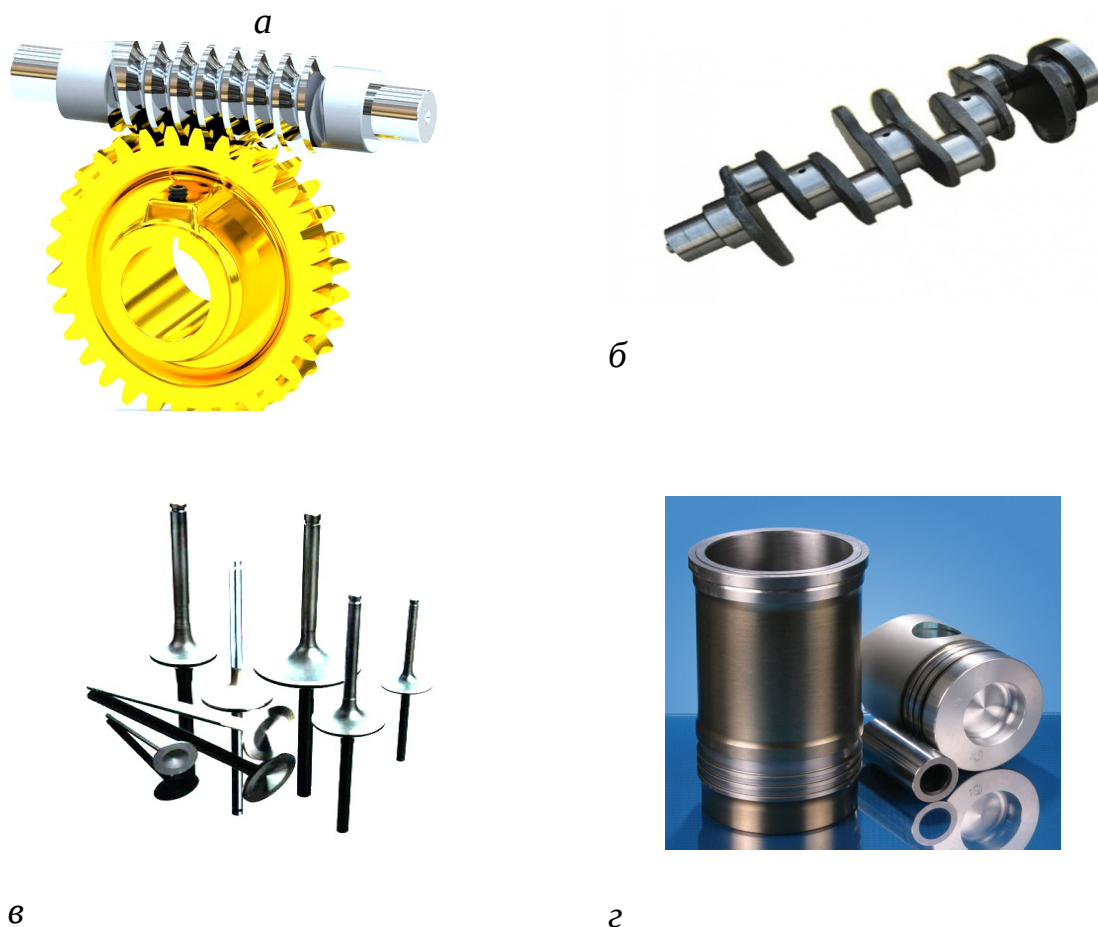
Примеры деталей с рабочими поверхностями сложной формы: а – червячная пара; б – коленчатый вал; в – клапан; г – гильза, поршень, поршневой палец
